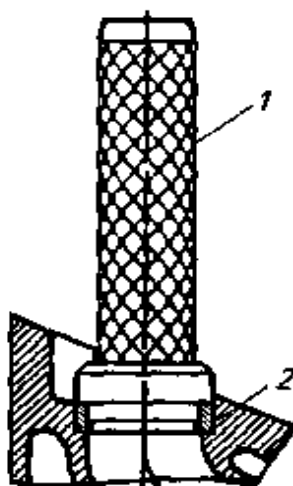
Запрессовка сідла клапана за допомогою оправки:
